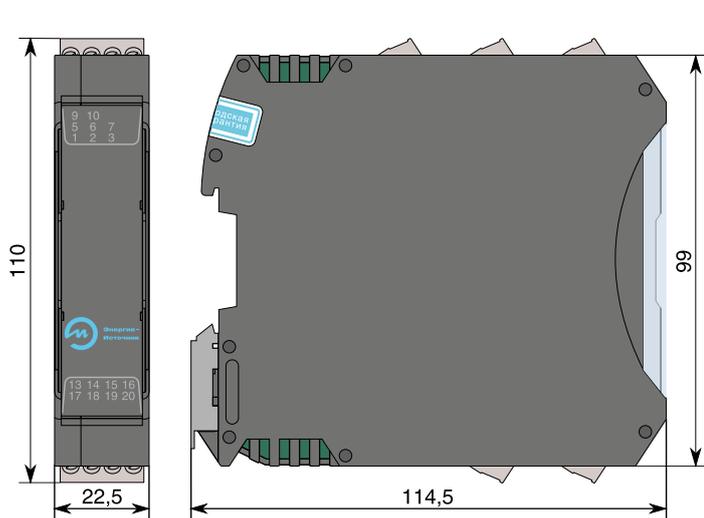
Габаритные размеры модуля в корпусе шириной 22,5 мм с разъемами с винтовыми клеммниками
